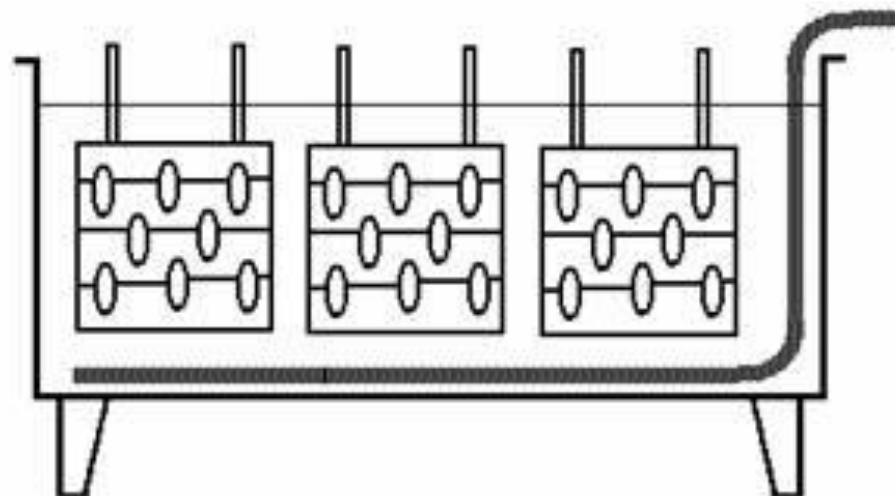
Расположение подвесочных приспособлений и змеевика по длине ванн
